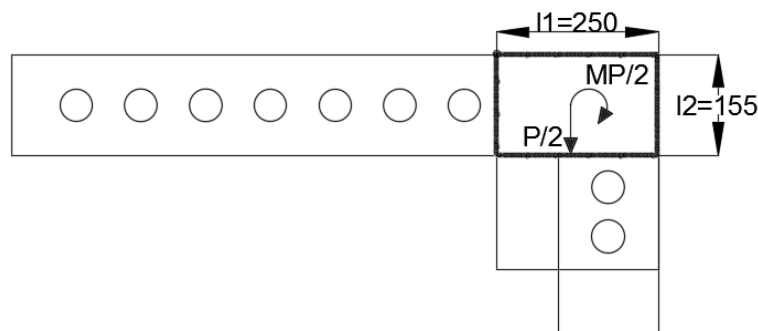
Unión del elemento diseñado sometido a soldadura. Fuente: Elaboración Propia
